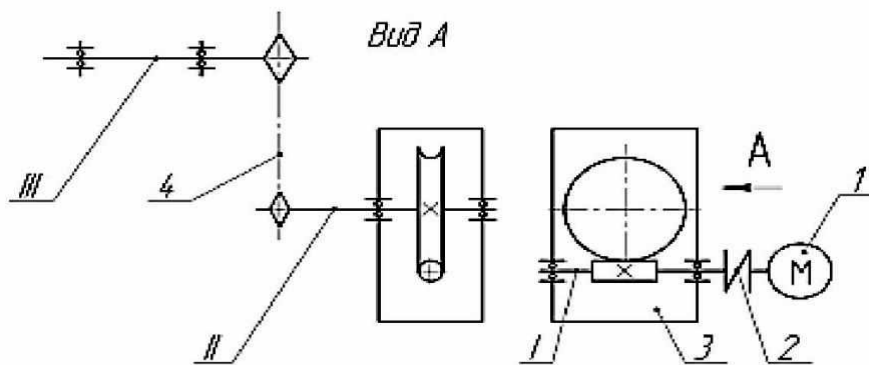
Привід до стрічкового конвеєра: 1 – електродвигун; 2 – муфта пружна; 3 – черв'ячний редуктор; 4 – ланцюгова передача; I – провідний вал редуктора; II - ведений вал редуктора; III - вал приводного барабана
